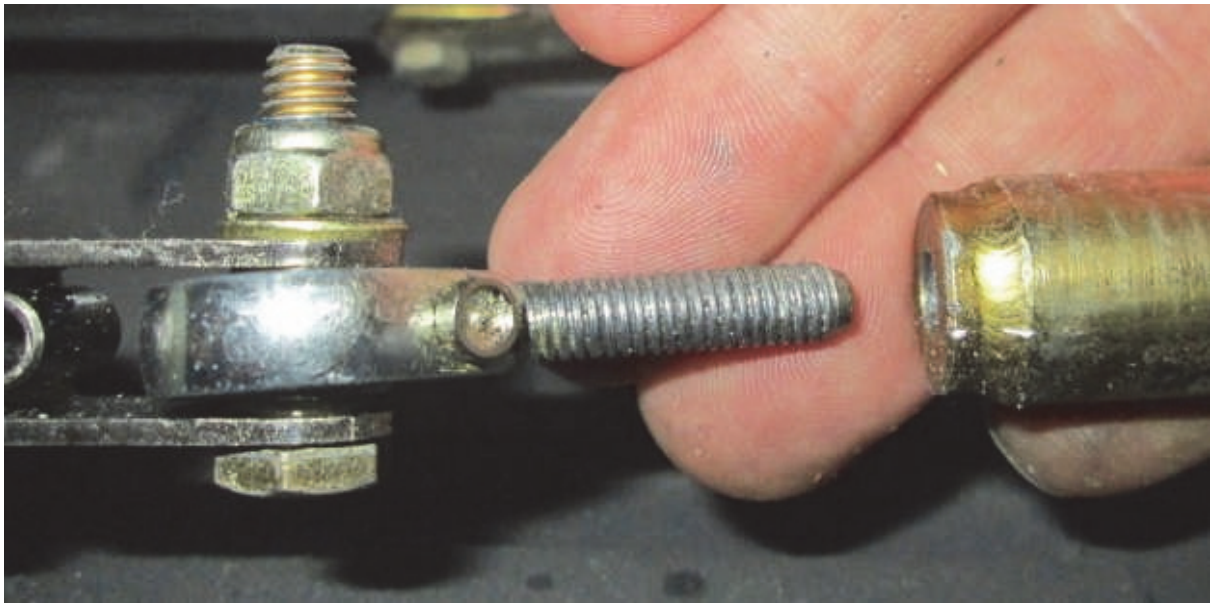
herausgerissener Gelenkstangenkopf mit Rechtsgewinde / *torn out rod end with right hand thread.
